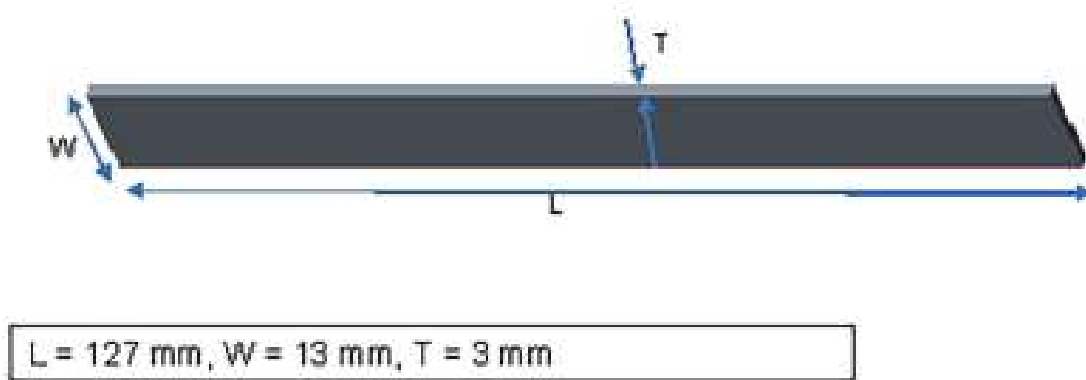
Dimensões da amostra segundo ASTM D 790.
